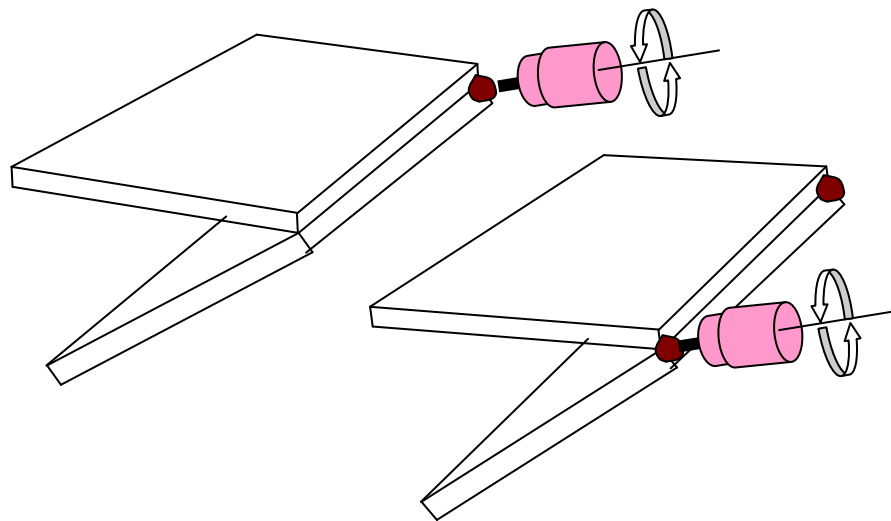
Punteado de las placas para obtener el ensamblaje de una junta de esquina, en posición horizontal.
